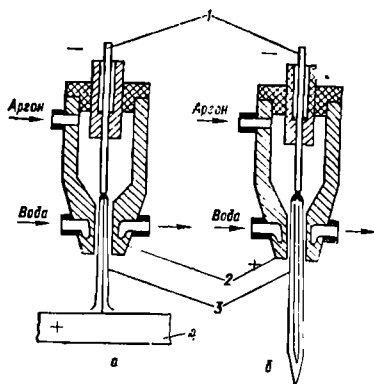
Сварочные плазмотроны прямого (а) и косвенного (б) действия.
